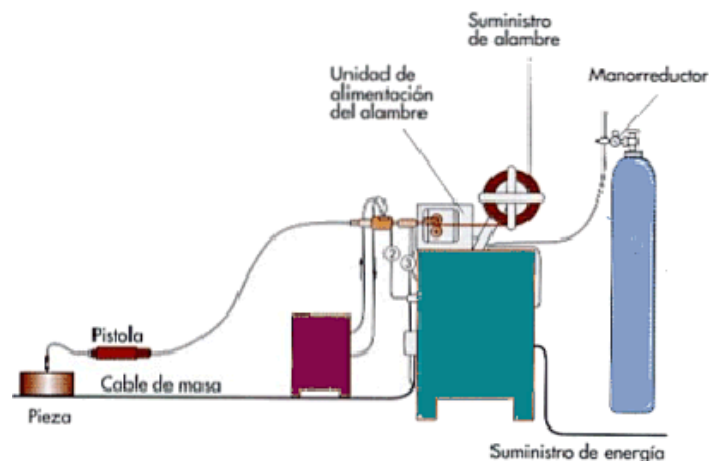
Circuito de soldadura para el proceso FCAW
